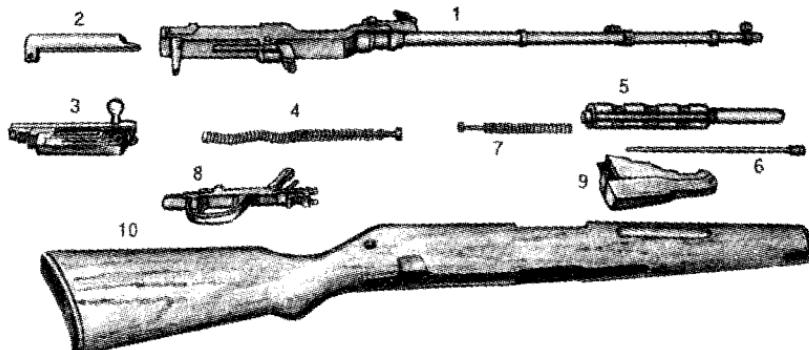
Неполная разборка СКС: 1 - ствол со ствольной коробкой и прицельным приспособлением; 2 - крышка ствольной коробки; 3 - затвор; 4 - возвратный механизм; 5 - газовая трубка со ствольной накладкой; 6 - газовый поршень; 7 - толкател с пружиной; 8 - ударно-спусковой механизм; 9 - магазин; 10 - ложа.
